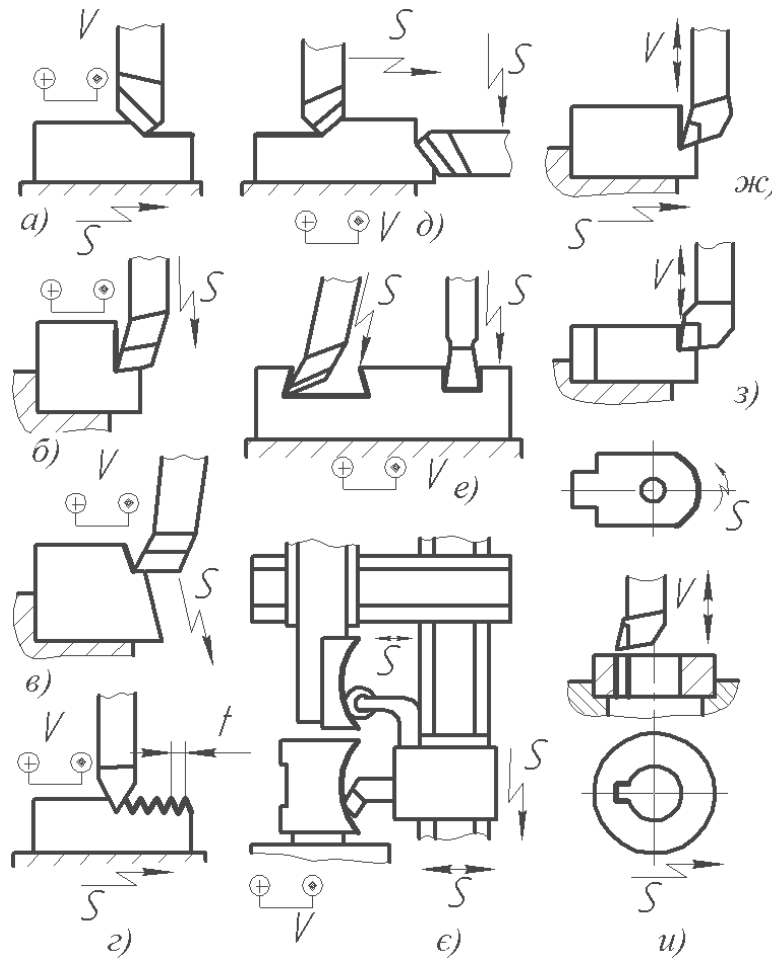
Схеми оброблення поверхонь заготовок на стругальних і довбальних верстатах
